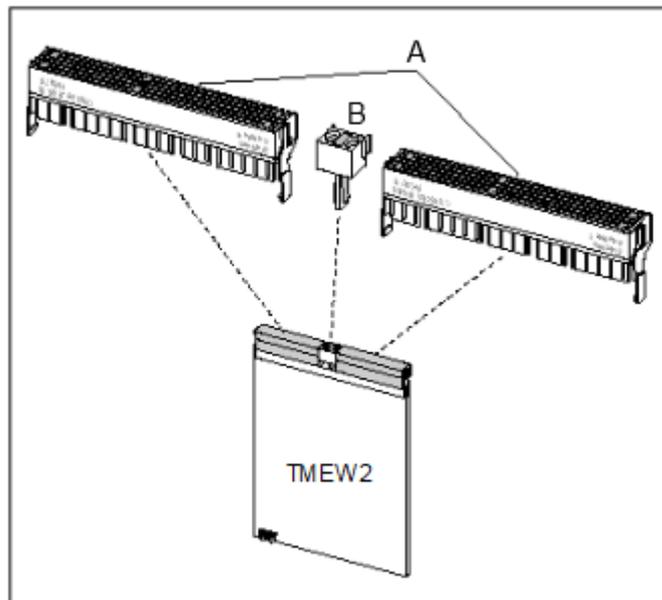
SIVAPAC-SIPAC-Baugruppenadapter
